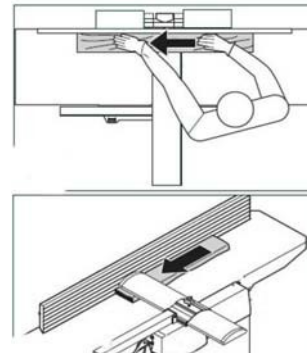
Réglage et guidage du matériau Rabotage de surface
